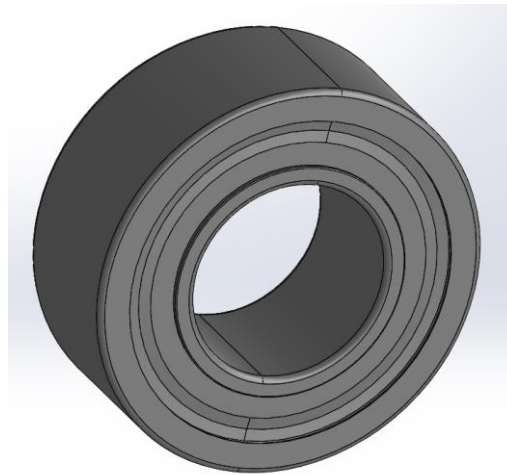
Diseño CAD del rodamiento SKF™ WBB1-8705R-2Z
